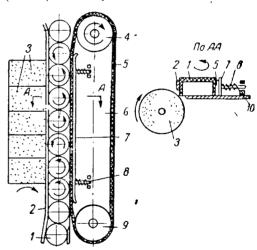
Универсальный полуавтоматический станок для обработки круглых изделий:
